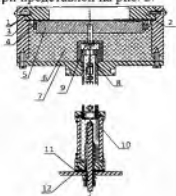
Конструкция устройства, формирующего внеэлектродный газовый разряд 1 - корпус, 2 - анодное кольцо, 3 - анод-сетка, 4 - фторопластовая прокладка, 5 - катод, 6 - изолятор
